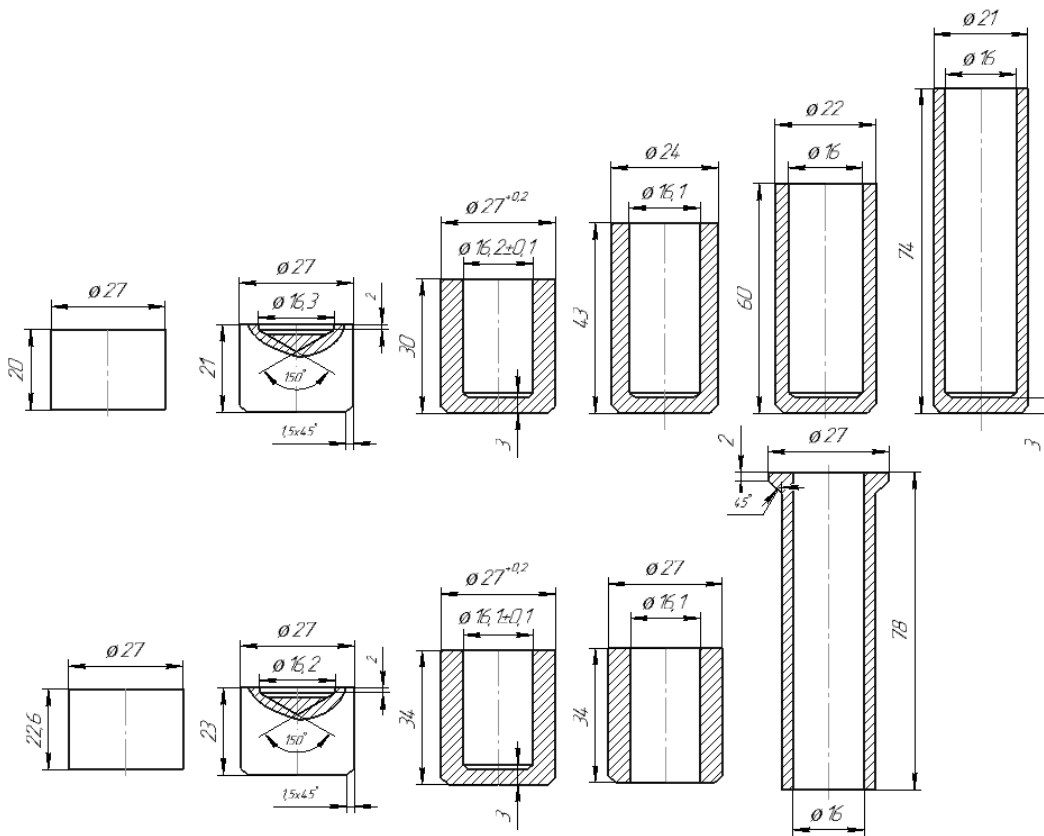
Послідовність виготовлення порожнистих деталей
